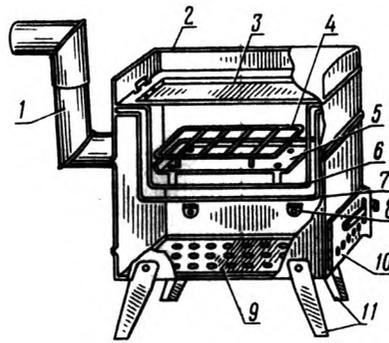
Устройство универсальной туристской печи: 1 — дымовая труба, 2 — крышка корпуса, 3 — крышка-сковорода, 4 — сетка (решетка), 5 — поддон, 6 — малый резервуар, 7 — большой резервуар, 8 — опоры для установки колосниковой решетки (четыре штуки), 9 — съемная колосниковая решетка, 10 — топочная дверца, 11 — складные ножки.
